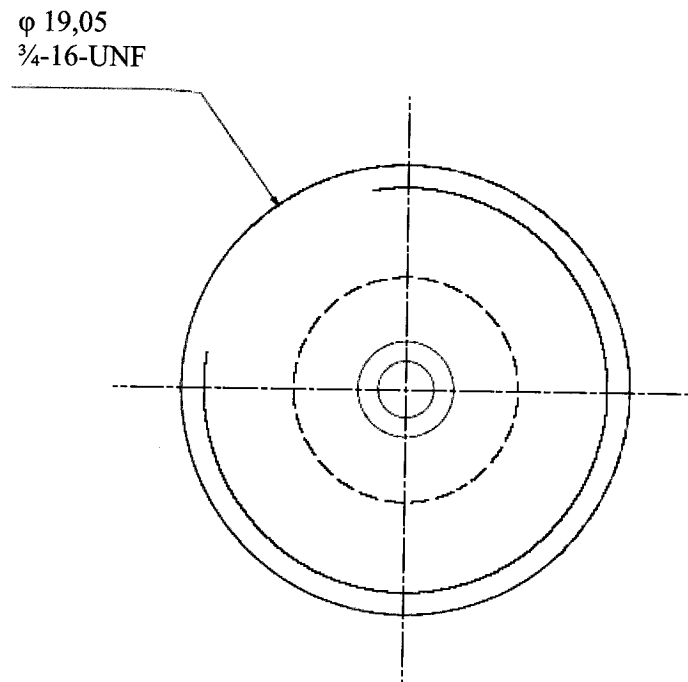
Dimensions de l'éprouvette de fatigue avec canal, exprimées en millimètres
